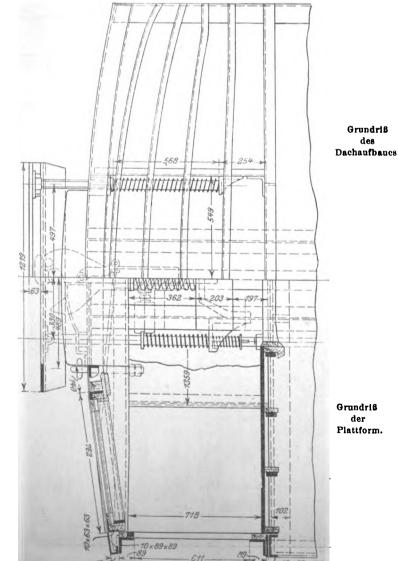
Dachspriegel bei elliptischem Dachaufbau.
